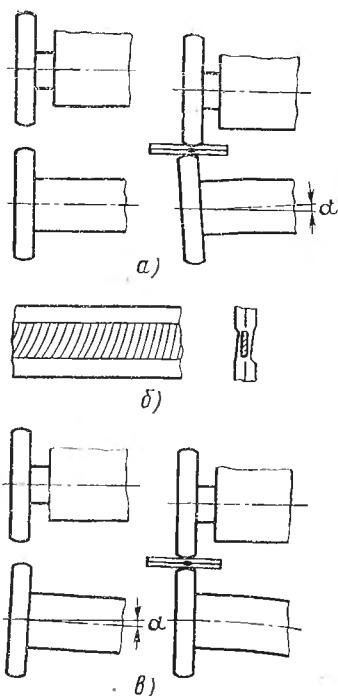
Устранение сдвига роликов при шовной сварке
